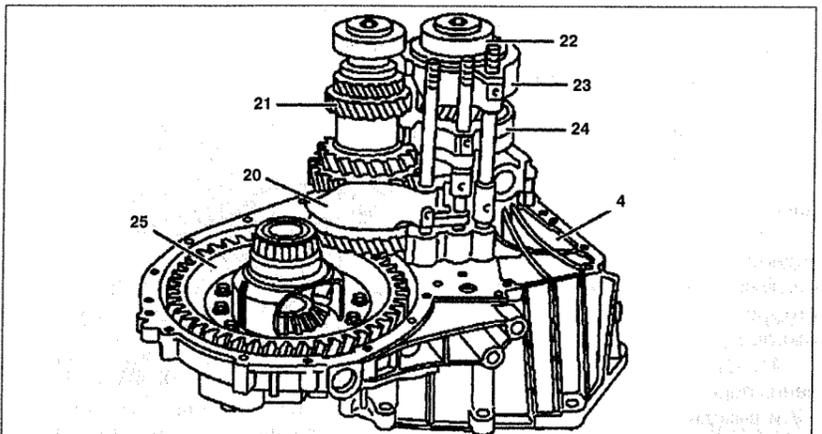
Разборка и сборка коробки передач (автомобили с двигателями 111.948 и 601.970): 20. Вилка включения 1-й и 2-й передач, 21. Выходной вал, 22. Ведущий вал, 23. Вилка включения 5-й передачи, 24. Вилка включения 3 и 4-й передач, 25. Дифференциал.
